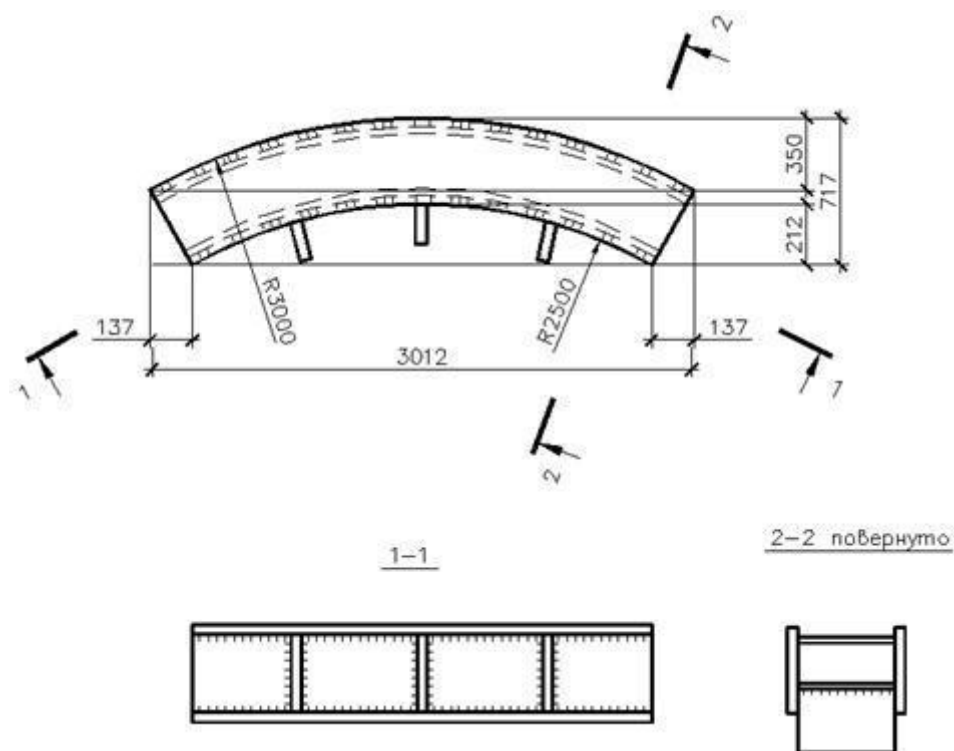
Разрез с секущей цилиндрической поверхностью
